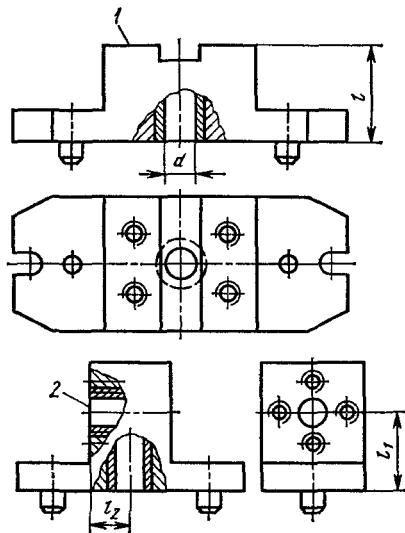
Унифицированные конструктивные элементы для установки СП на стол станка с ЧПУ
